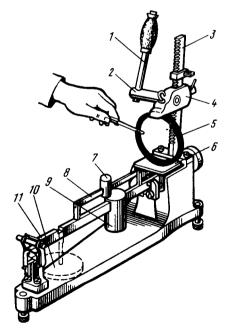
Прибор для проверки упругости поршневых колец и пружин:
